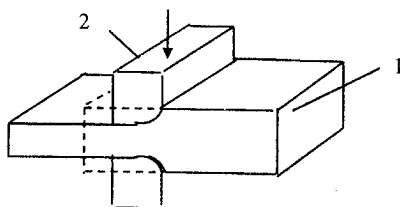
Схема протягування 1 – заготовка; 2 – пуансон; 3 – деталь.
